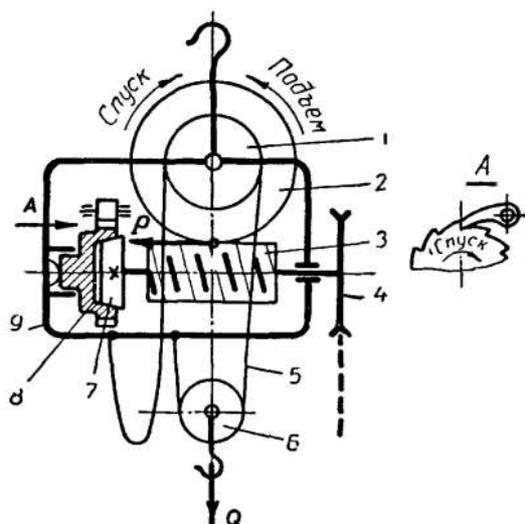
Грузоупорный тормоз червячной тали.
